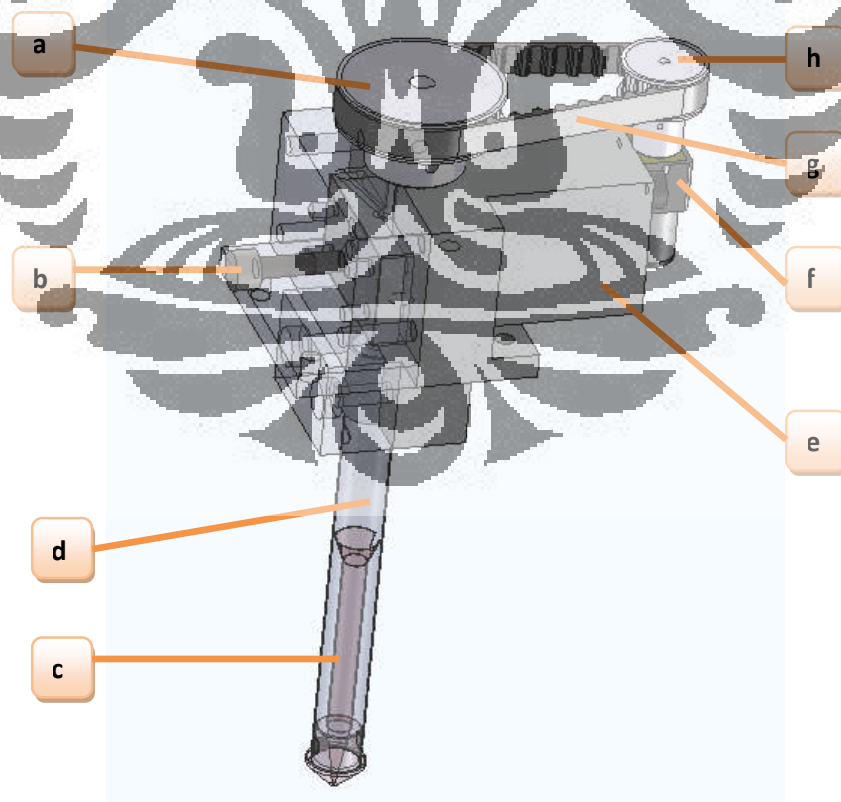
Komponen mesin *rapid prototyping
